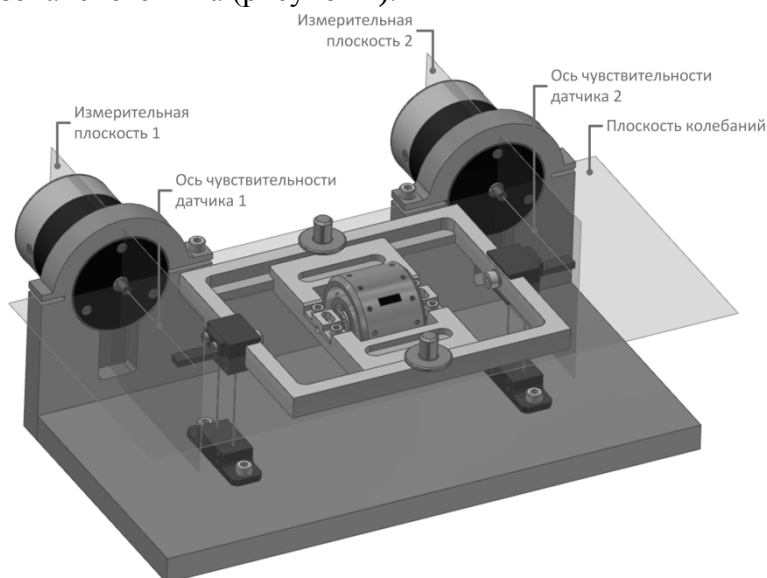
Механическая часть зарезонансного балансировочного станка
